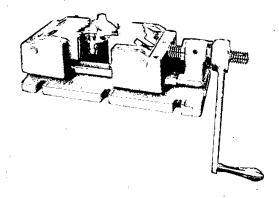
Hilti-Universalspannwerkzeug (Hahn & Kolb, Stuttgart)
